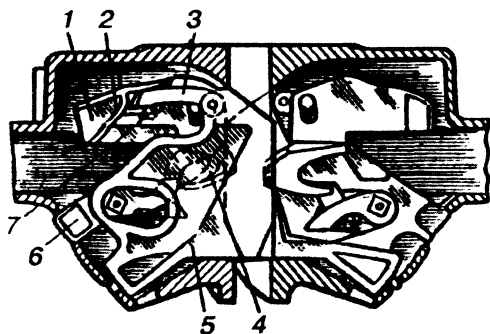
Положение деталей механизма сцепленных автосцепок
